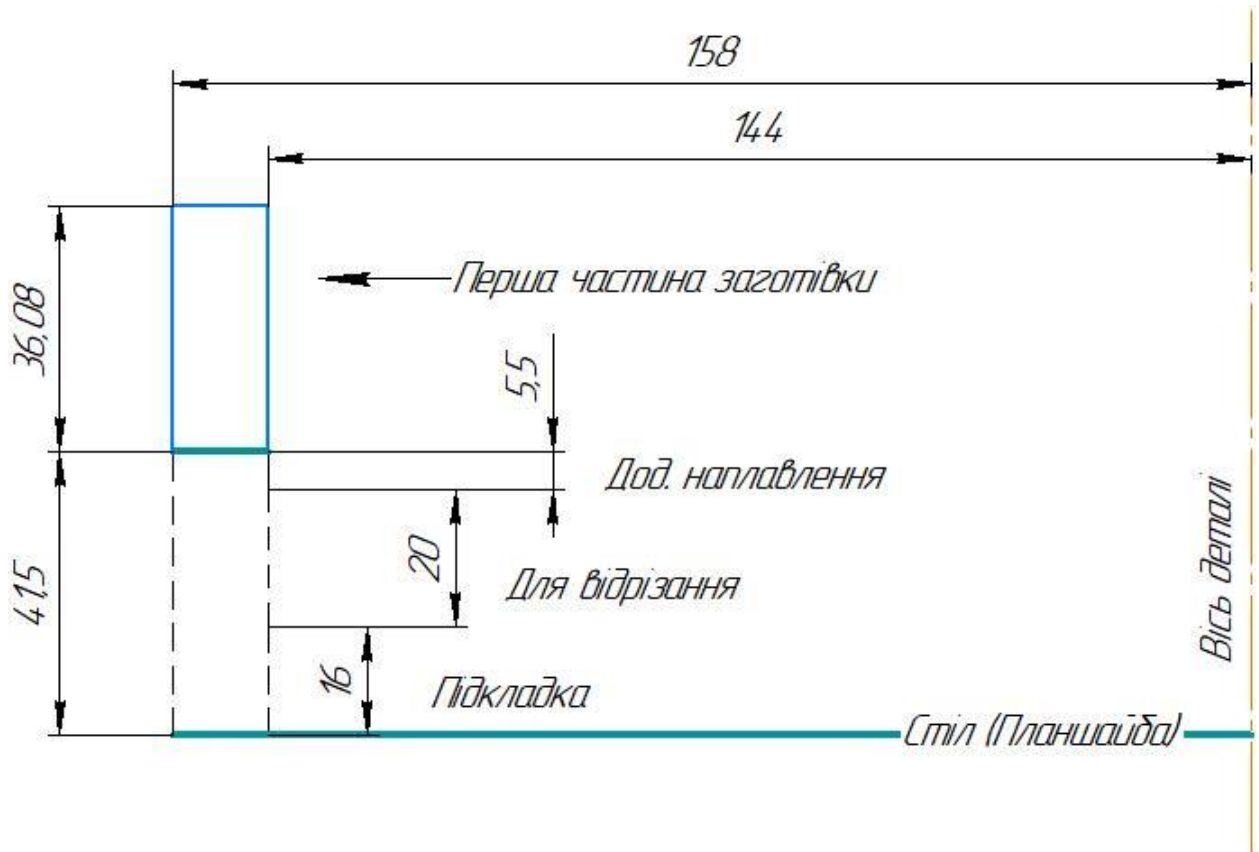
Креслення першої частини заготівлі 4500301001 (Зроблено в КОМПАС-3D v17)
